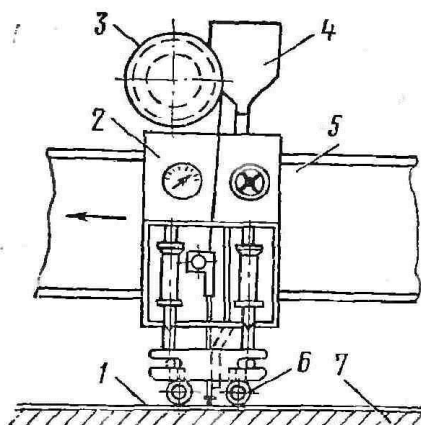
Приспособление для сварки обшивки боковых стен кузова:
